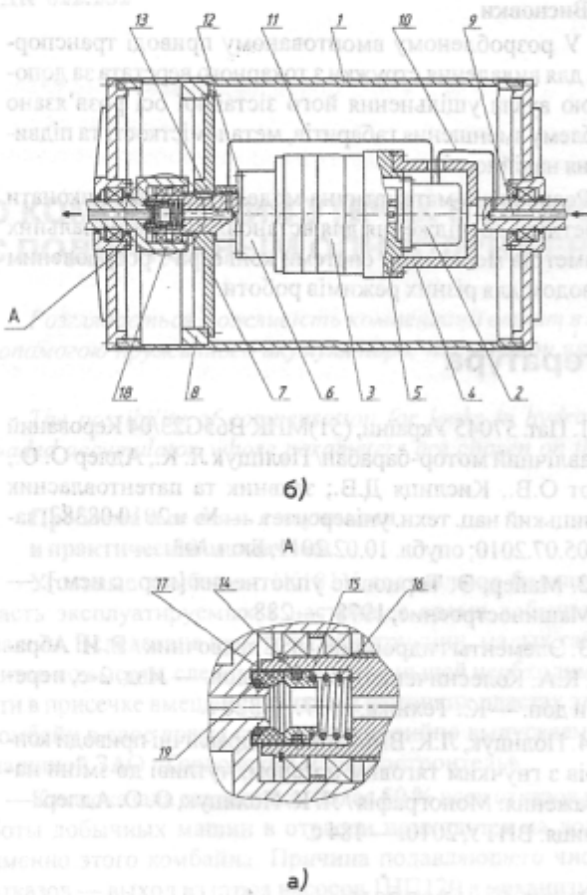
Конструктивна схема вмонтованого привода конвеєра для видалення стружки з верстата.
